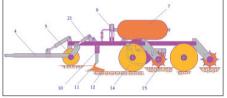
Многофункциональный комбинированый агрегат для обработки почвы импульсным воздействием ударной волны: 1,3 — складывающиеся секции; 2 — базовая секция; 4 — сница; 5 — опорные колеса; 6 — транспортные колеса; 7 — баллон сжатого воздуха; 8 — полый вал; 9 — система пуска сжатого воздуха; 10 — полые ступицы; 11 — стойка; 12 — культиваторные лапы; 13 — пневмотрубка с выпускным клапаном; 14 — дисковые фрезы; 15 — бороны; 16, 18 — пневмоэлектроклапаны; 17 — микрорессиверы; 19 — поршень; 20 — цилиндр; 21 — винтовой механизм
